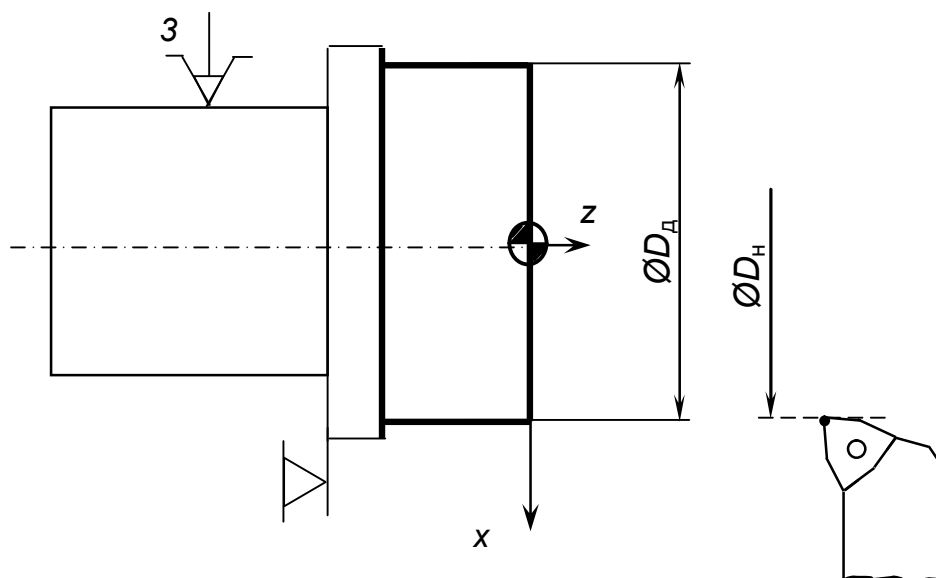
Схема, що пояснює процес розмірного настроювання токарного верстата
